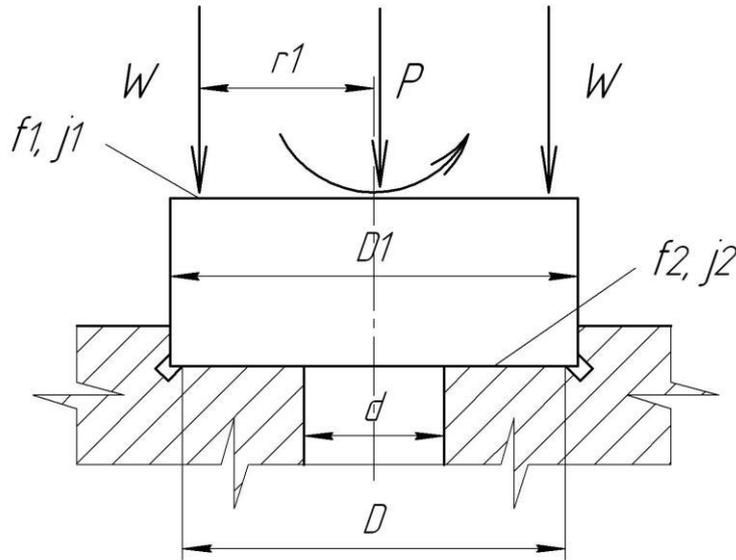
Схема сил действующих на заготовку при ее установке по наружной поверхности
